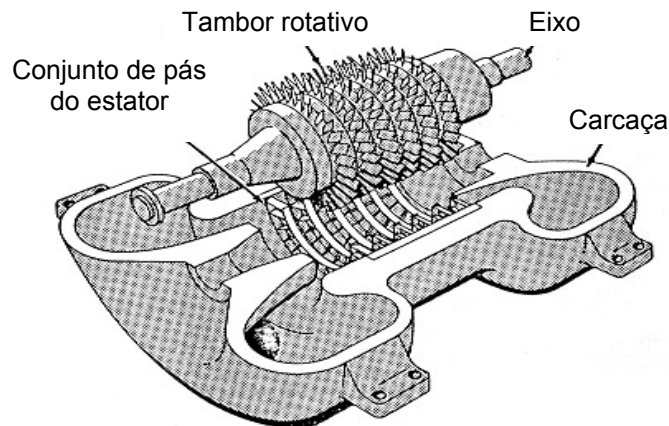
Compressor axial com detalhes do rotor e estator (RODRIGUES, 1991).
